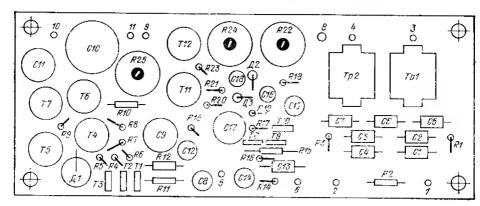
Монтажная схема платы усилителя НЧ-АРУ (вид сверху)
